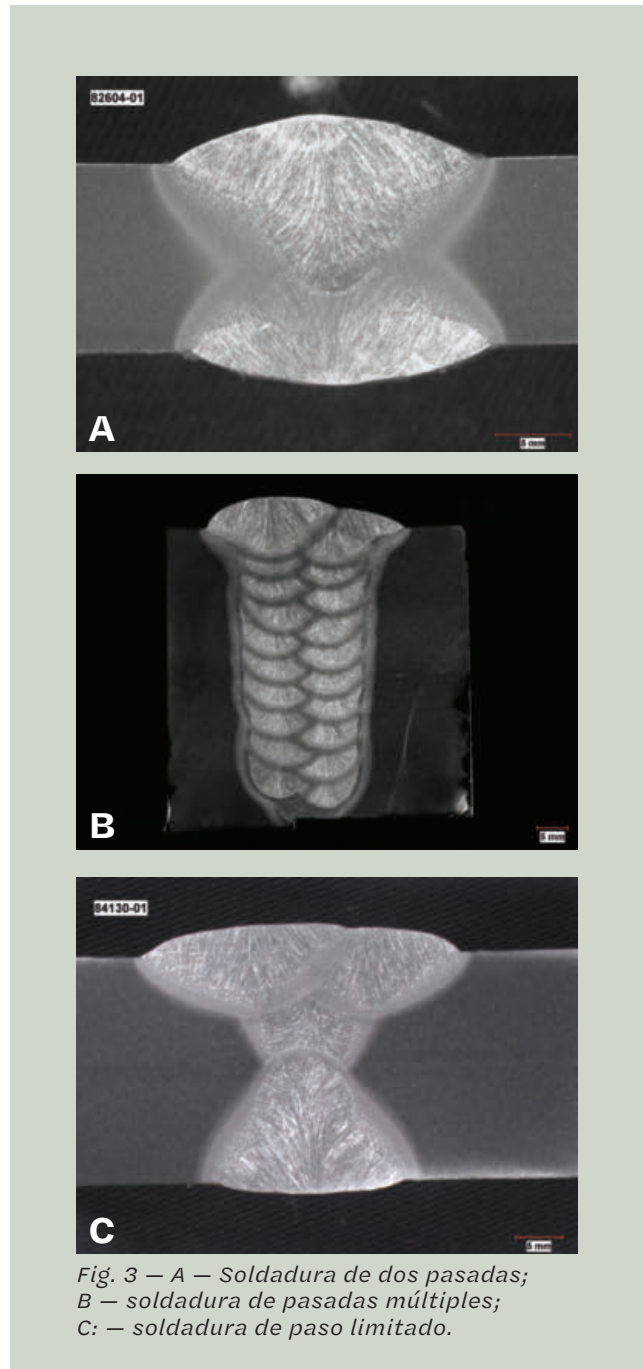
A — Soldadura de dos pasadas; B — soldadura de pasadas múltiples; C: — soldadura de paso limitado.
